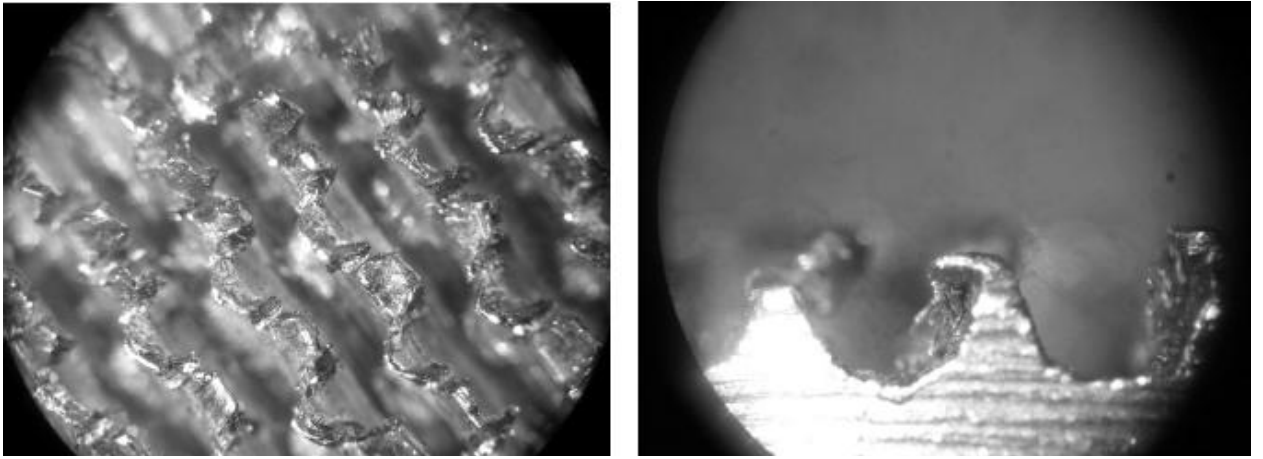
Внешний вид профиля рванной резьбы после накатки
